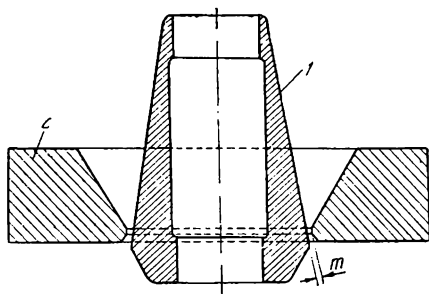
Мундштук и дорн для профилирования заготовок ездовых камер:
